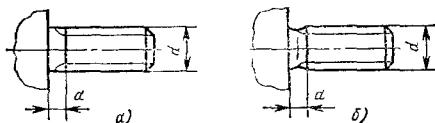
Форма недореза при выполнении наружной метрической резьбы:
